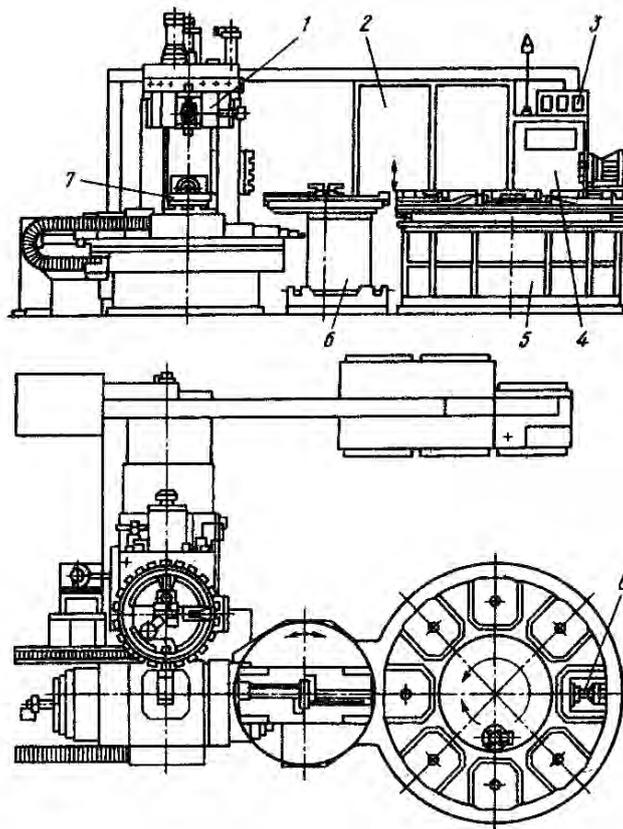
Компоновка ГПМ "Модуль-500" на базе многоцелевого станка ИР-500 МФ4:
